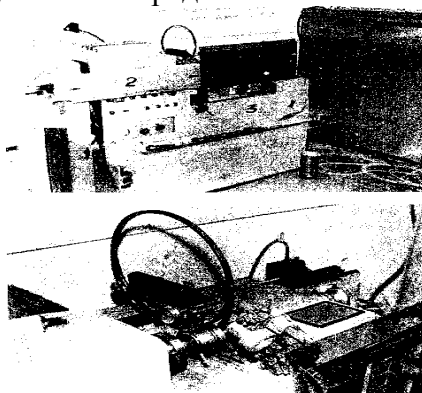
Общий вид лазерного технологического комплекса (а) и приспособления для обработки поршневых колец (б): 1 – генератор ЛТН – 103; 2 – излучатель; 3 – станок с ЧПУ; 4 – стойка ЧПУ; 5 – система фокусировки луча; 6 – приспособление для вращения кольца; 7 – поршневое кольцо
